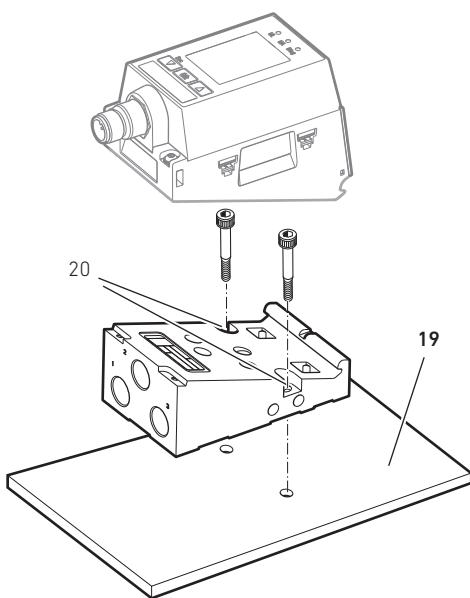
Montaje de la EV03 sobre una placa de montaje con tornillos en los orificios de paso superiores
